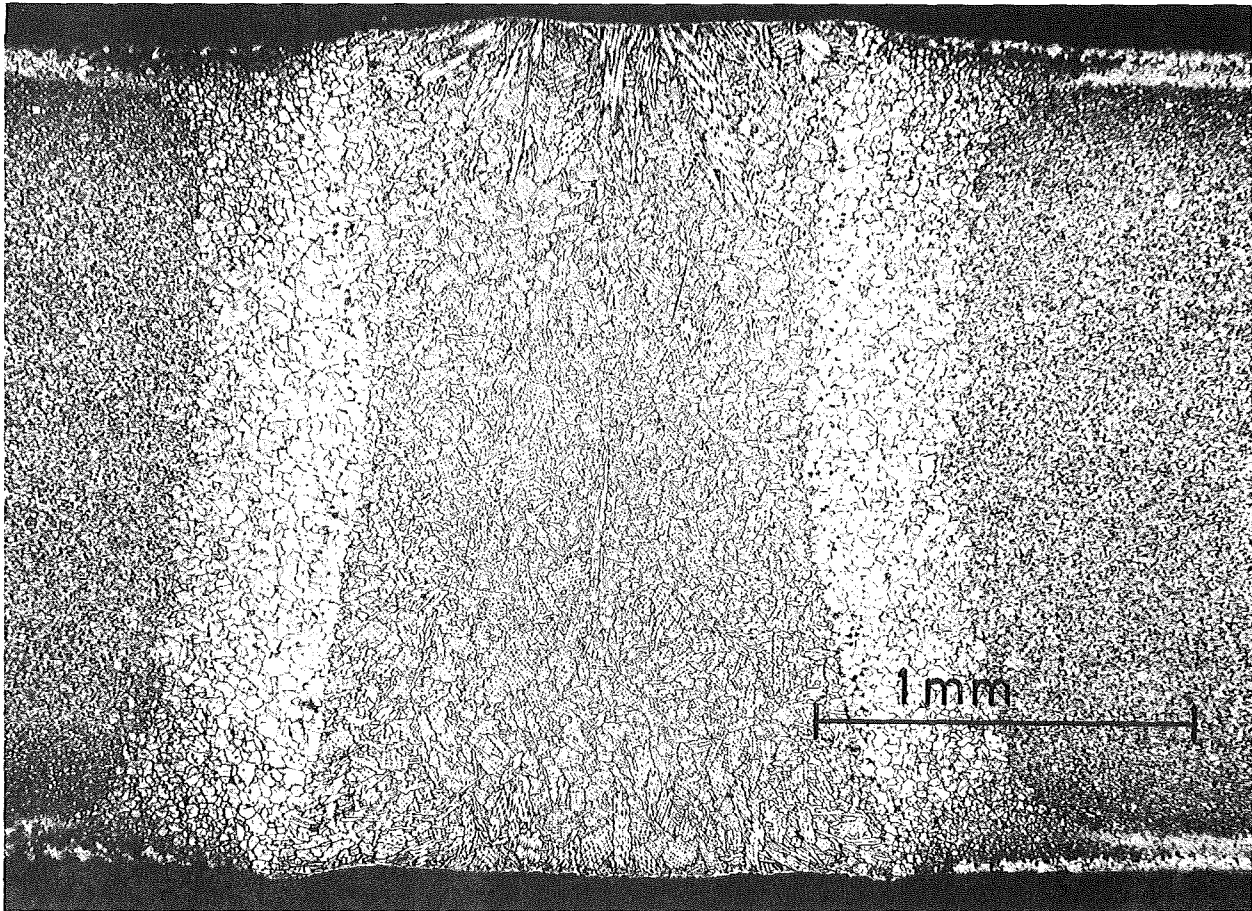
Tangentialer Anschliff der Probe 8A25 an der Endstopfenschweißnaht
